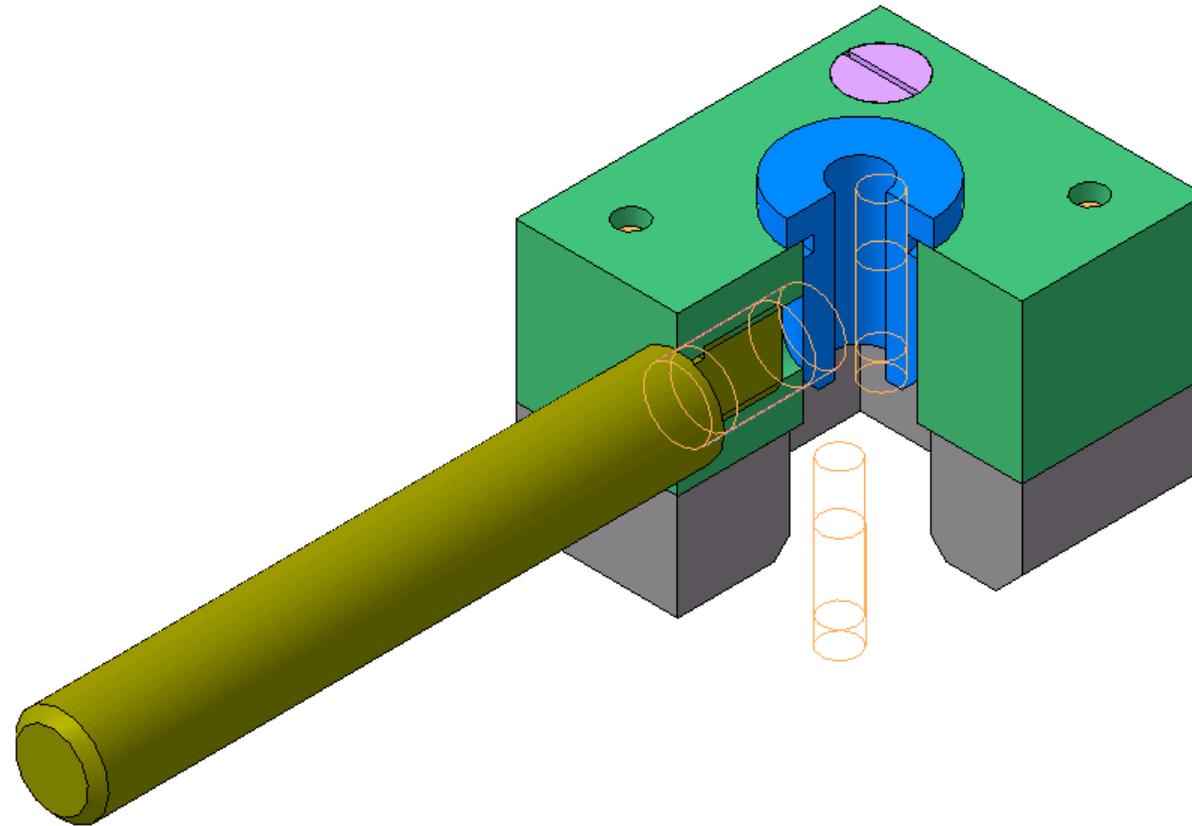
3D-модель сборки изделия «Кондуктор-2» (варианты 5, 25)
